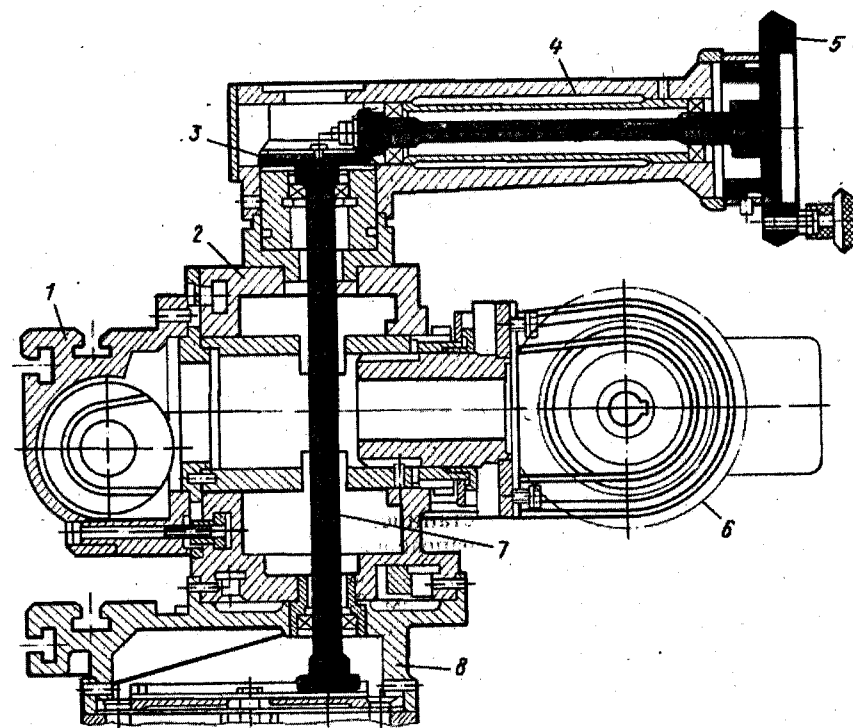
Шлифовальная бабка универсально-заточного станка
